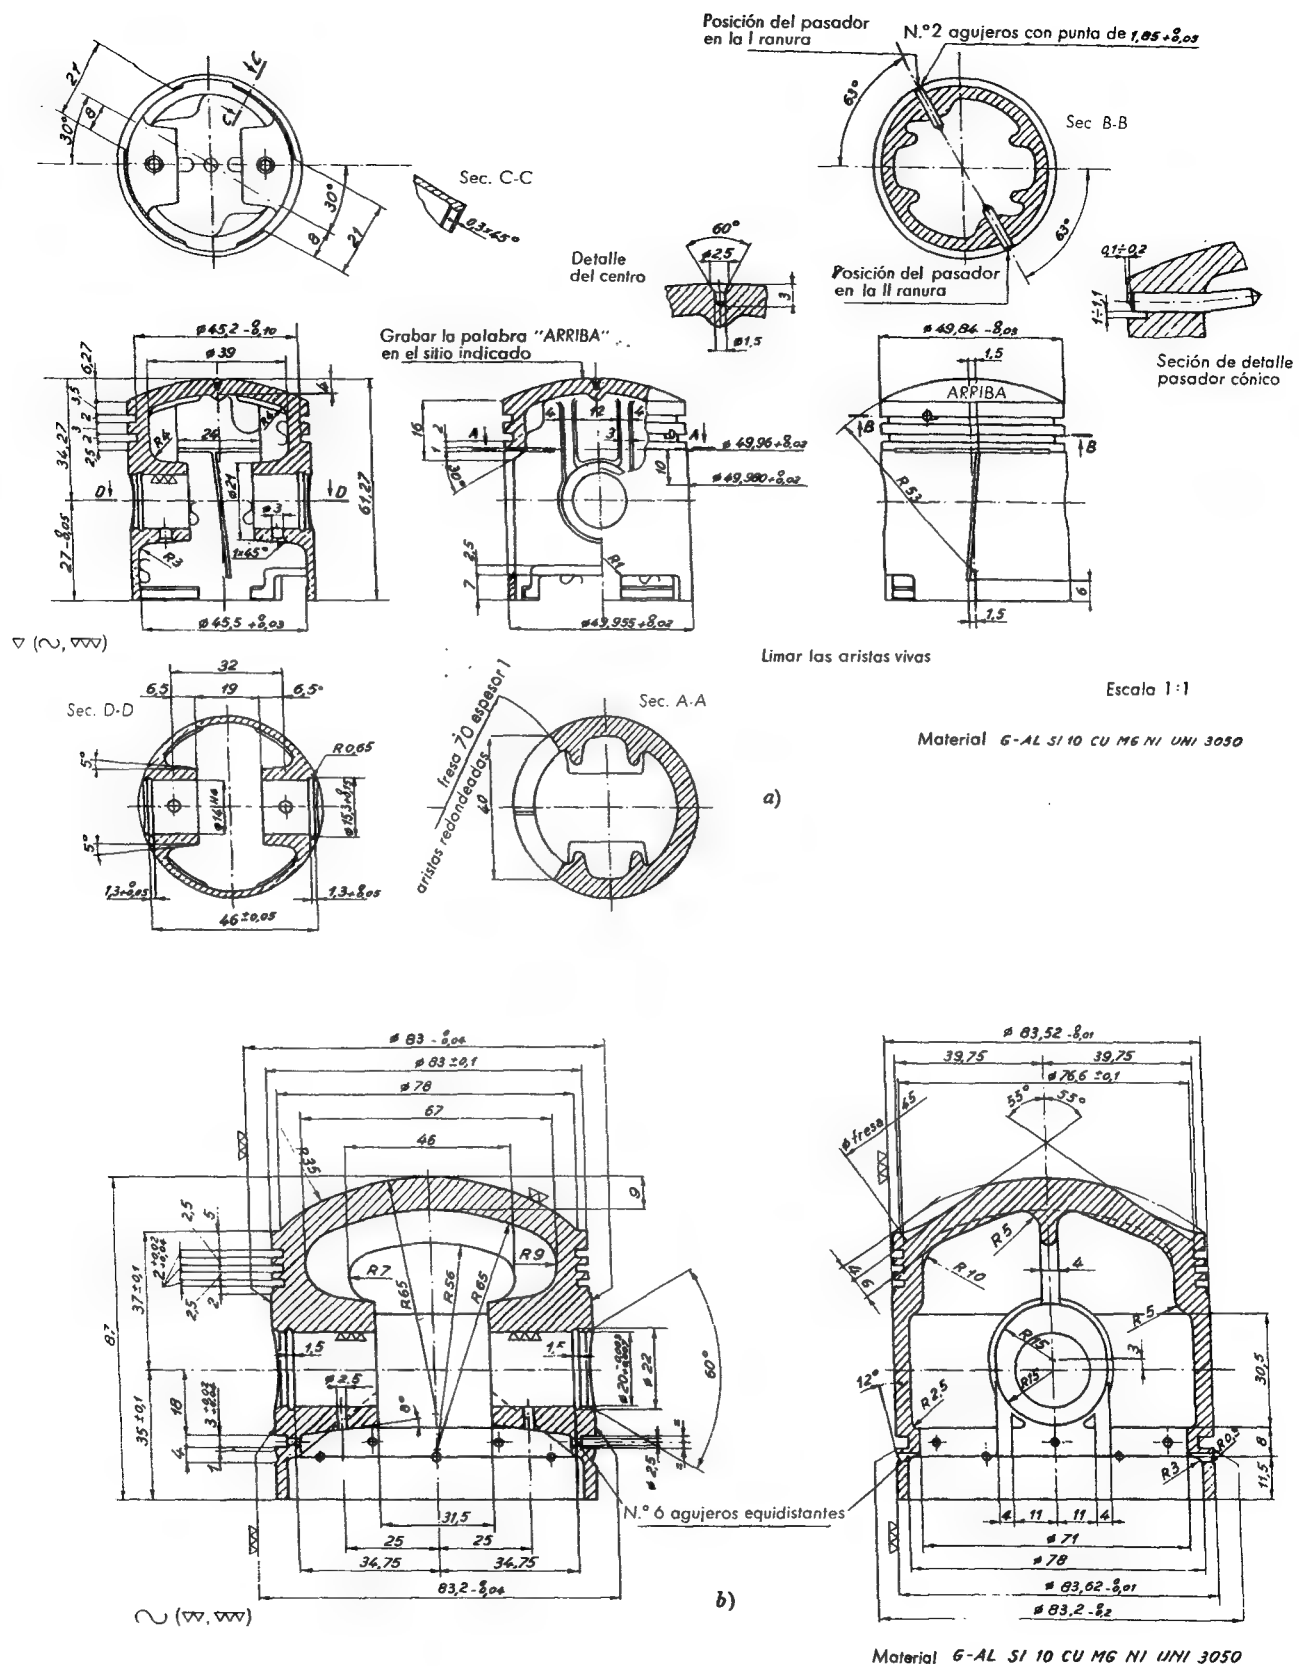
a, b. Pistones de motor para moto: a) Pistón de motor para moto de 4 tiempos (Guzzi); b) Pistón de motor para moto (Gilera).
